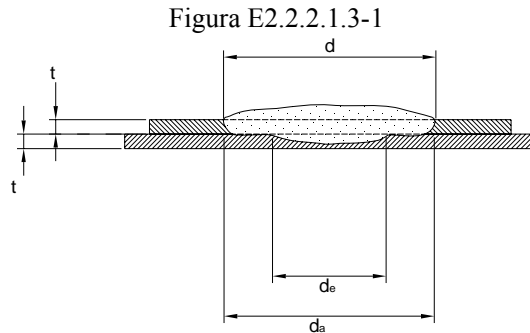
Puntos de soldadura por arco – Plancha a Plancha
